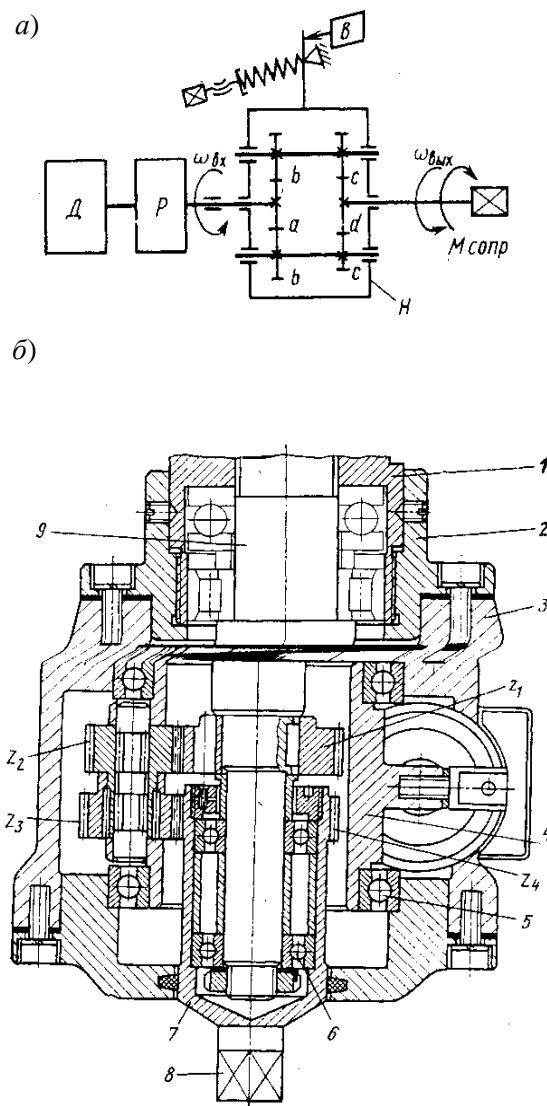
Принципиальная схема (а) и конструкция (б) планетарного редукторного динамометра
